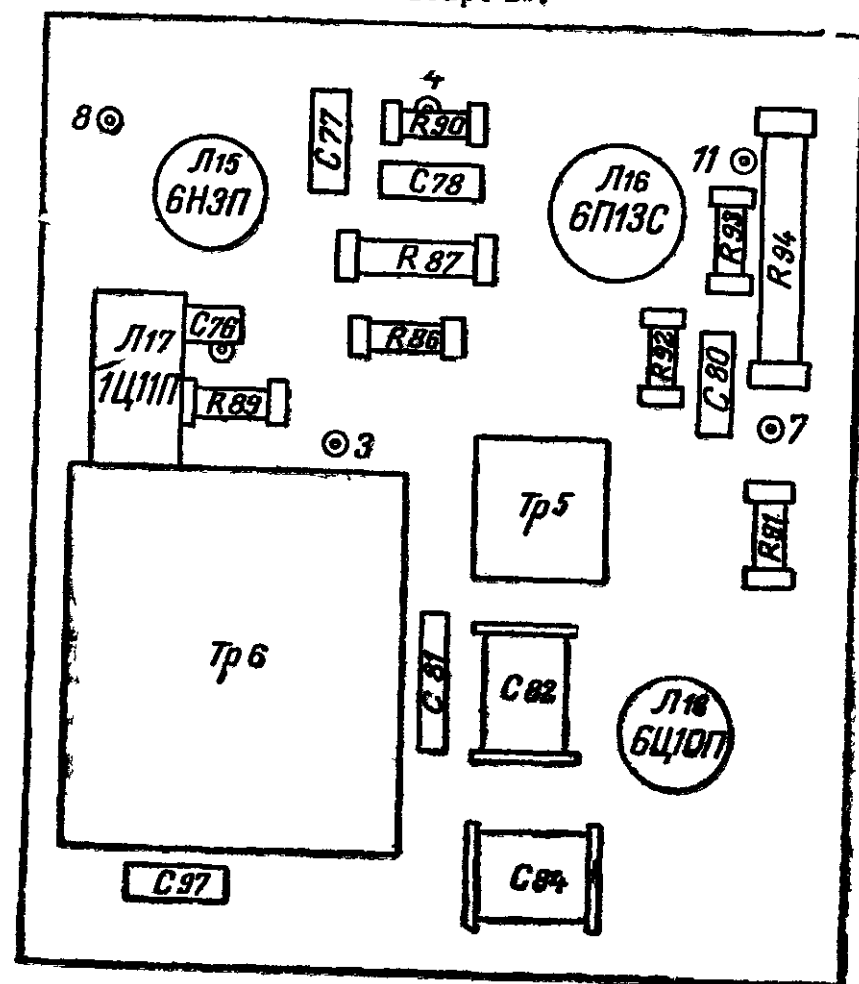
Монтажная схема блока строчной развертки телевизора «Старт-2»
